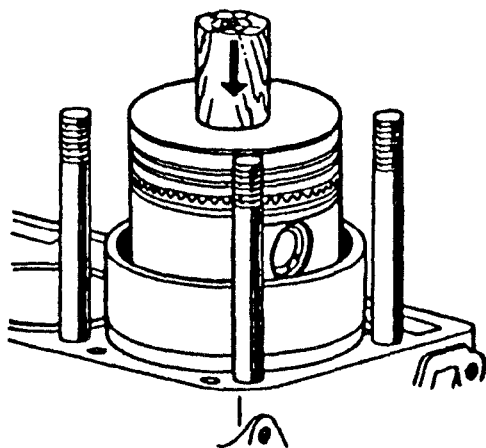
Установка поршня с кольцами в цилиндр с помощью оправки 6999-7685
